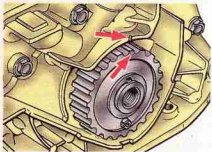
Проверка совпадения установочных меток на шкиве распределительного вала и задней защитной крышке
